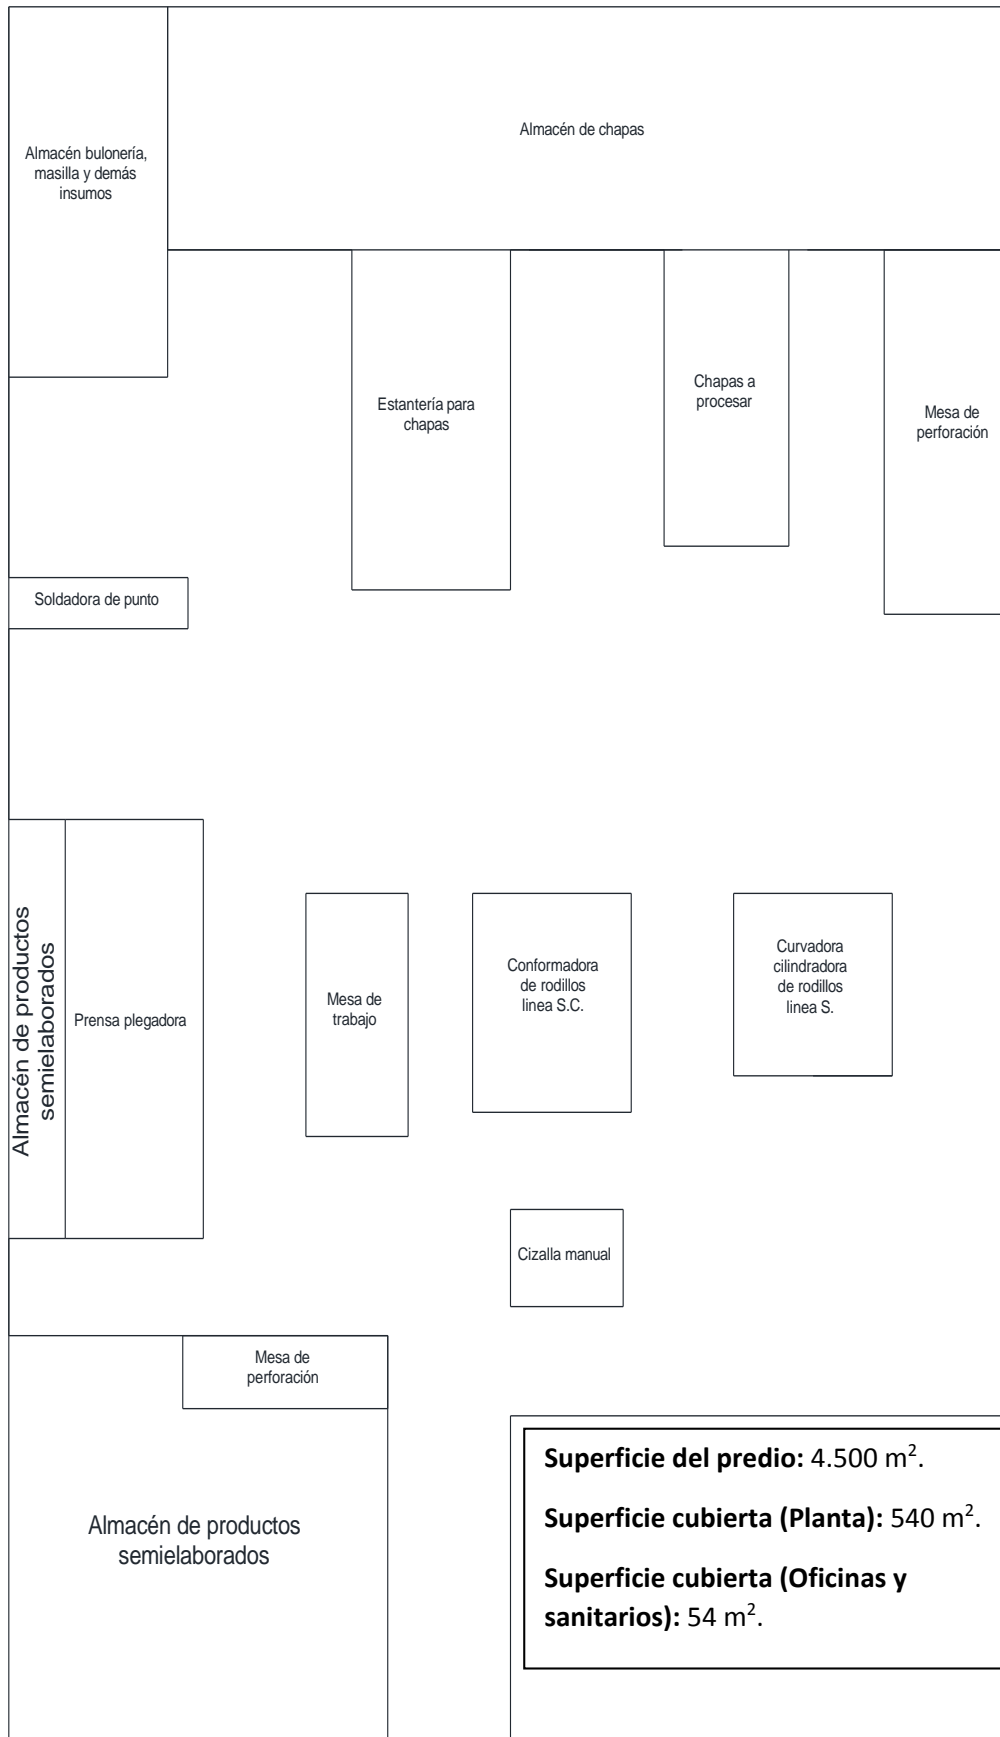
Layout del sector chapistería al inicio del proyecto.
